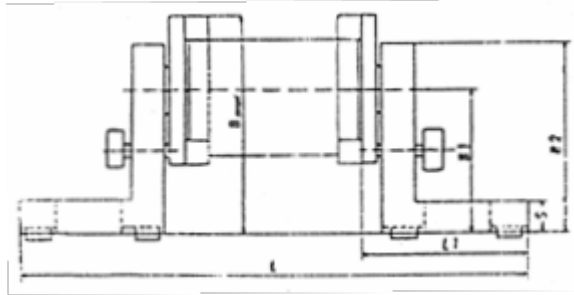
Jig Bor Kotak untuk mengebor valve
